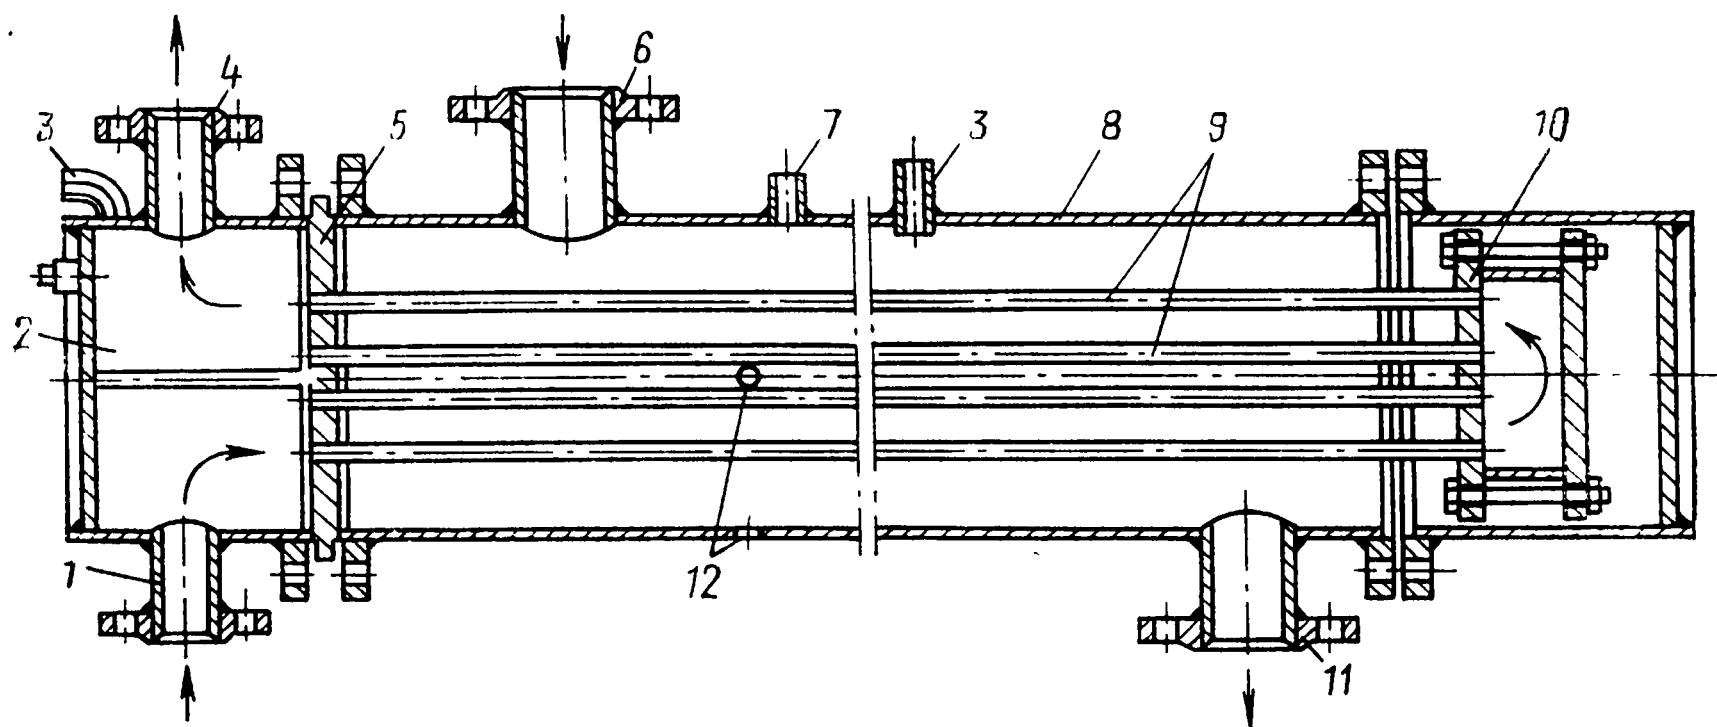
Нагреватель поверхностный пароводяной двухходовой
